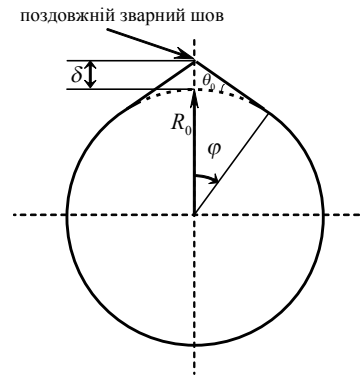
Поперечний переріз труби з кутовою неспіввісністю поздовжнього зварного шва
